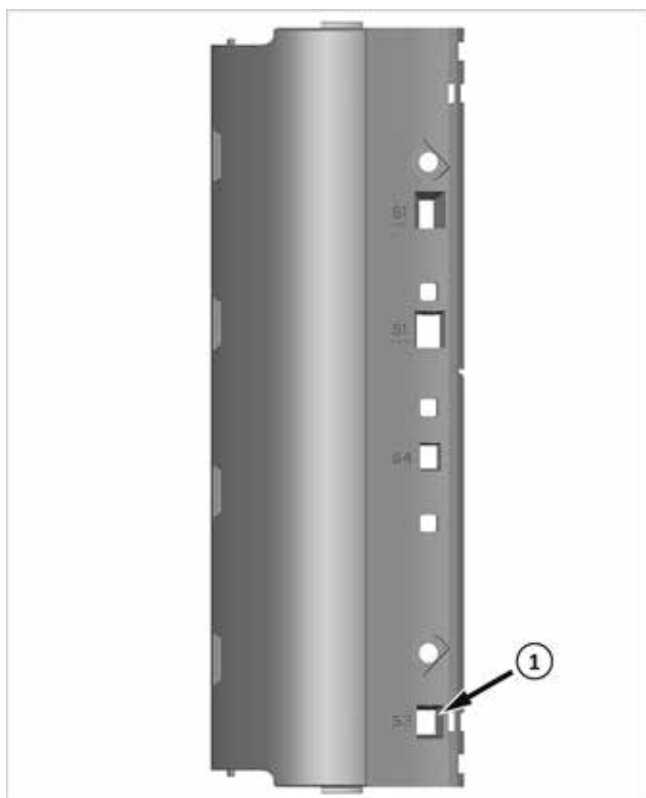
Aislamiento trasero del recipiente, lado izquierdo
